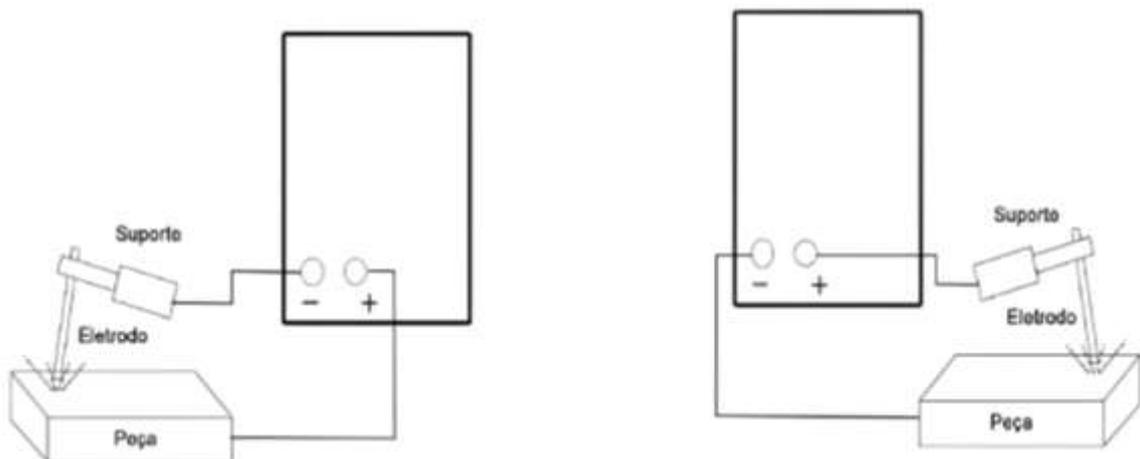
Conexão DCEP e DCEN do para soldagem com eletrodo revestido.
